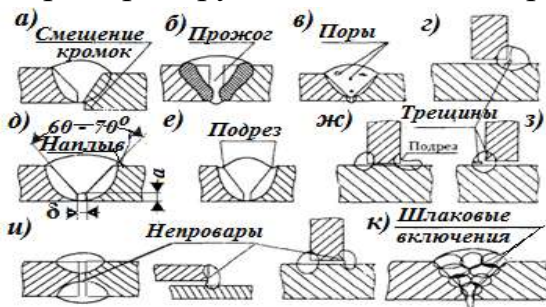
Разновидности дефектов швов при сборке и сварке плавлением
